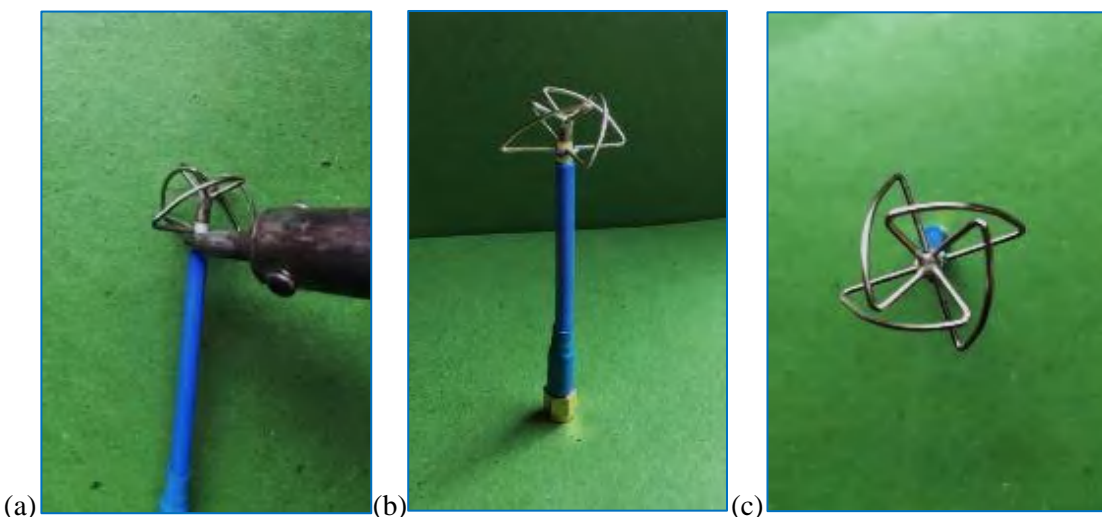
Antena tipo trébol (cloverleaf) terminada. (a) soldadura de los puntos al cable coaxial, (b)vista frontal terminada, (c) vista superior
